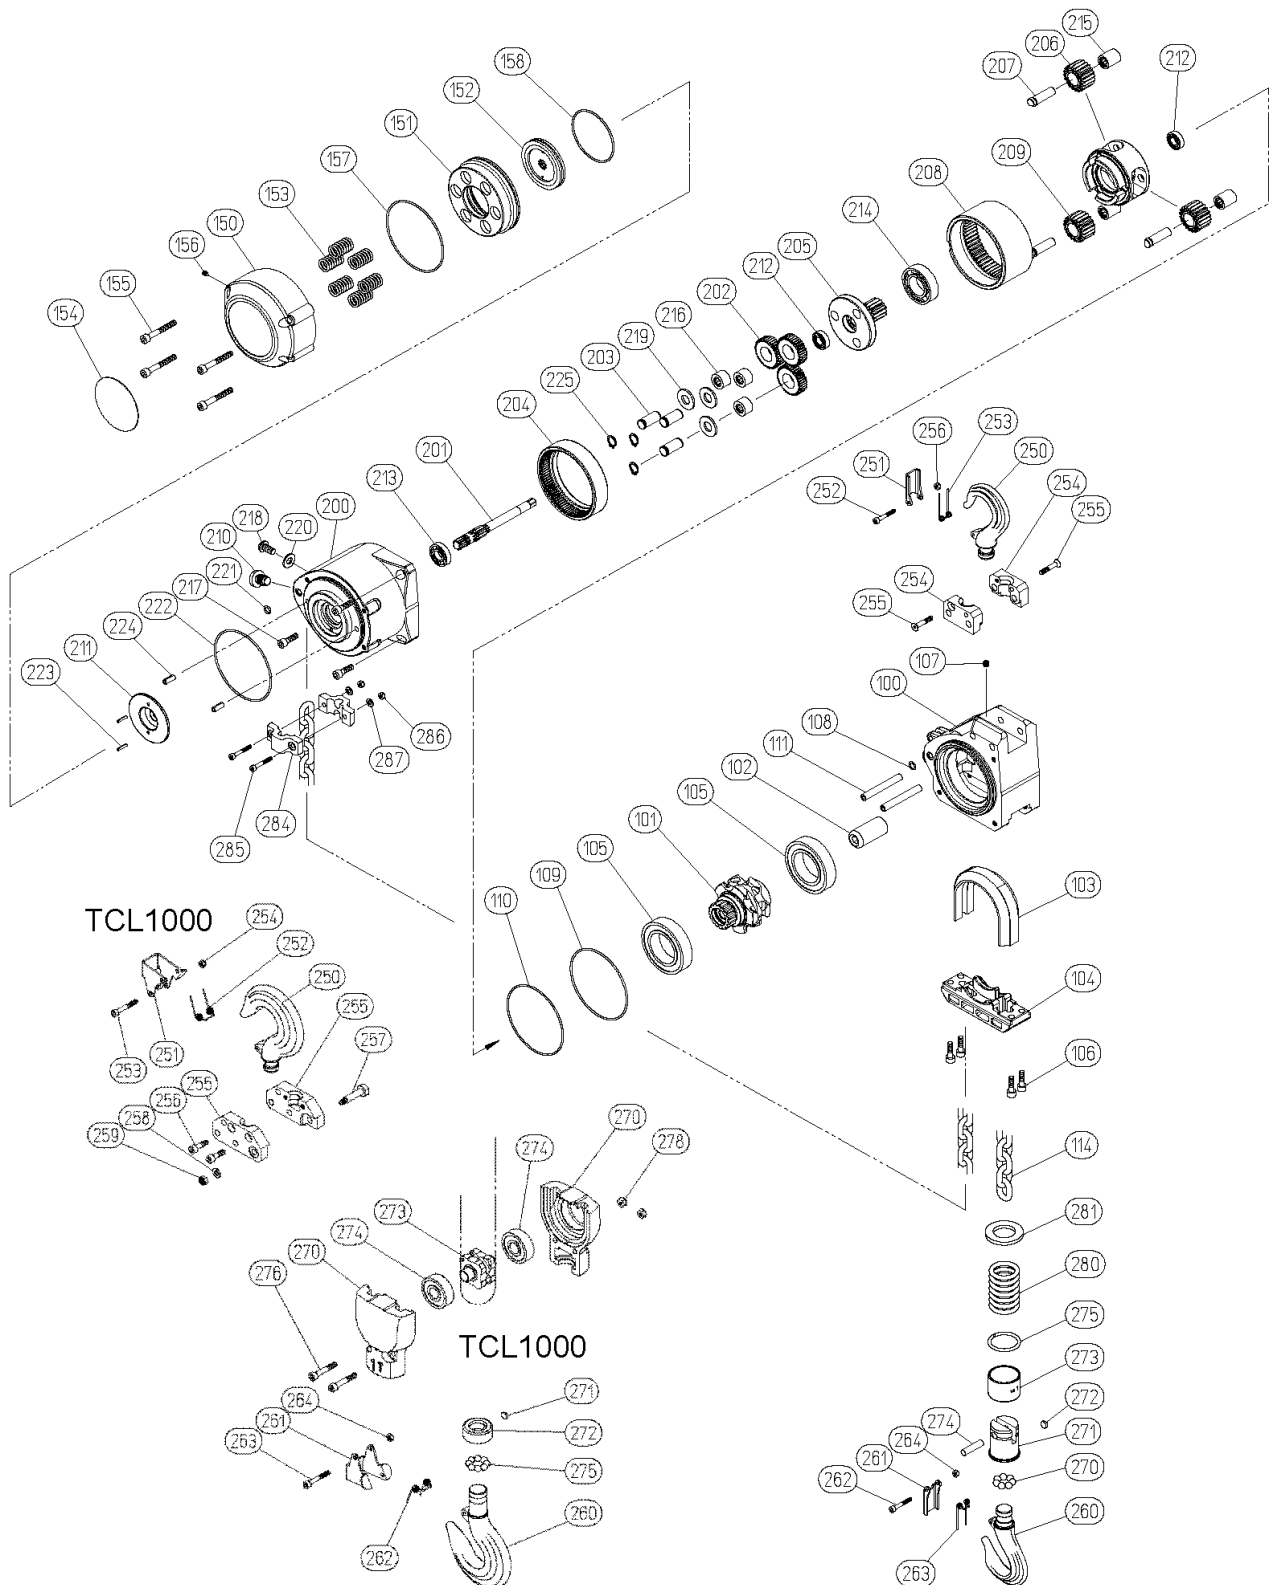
Componentes de frenos, engranajes y suspensión de carga
